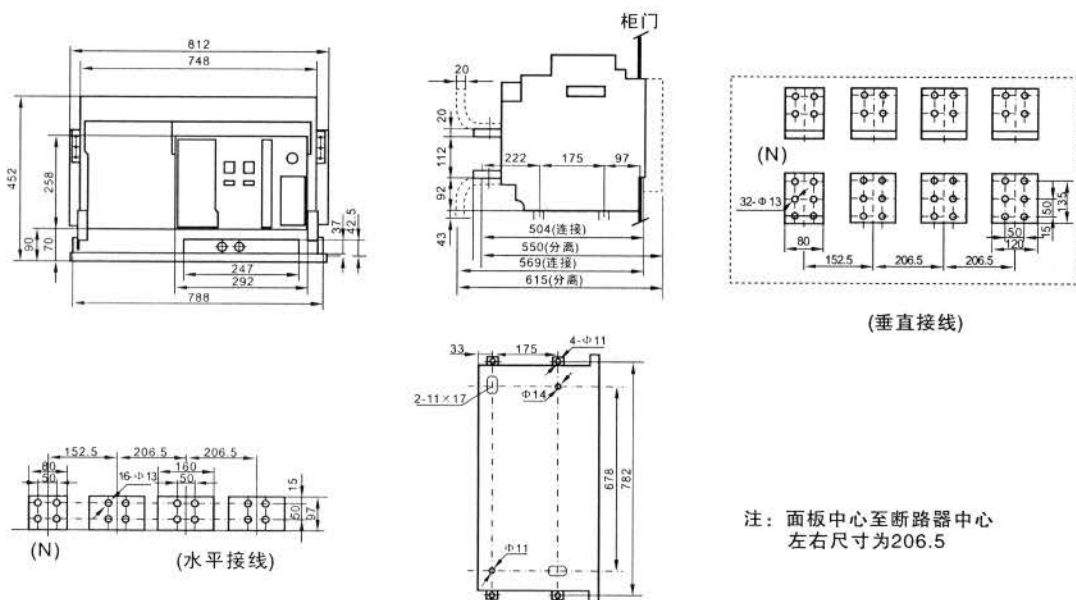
抽屜式断路器安装尺寸及外形尺寸(4000/4)
